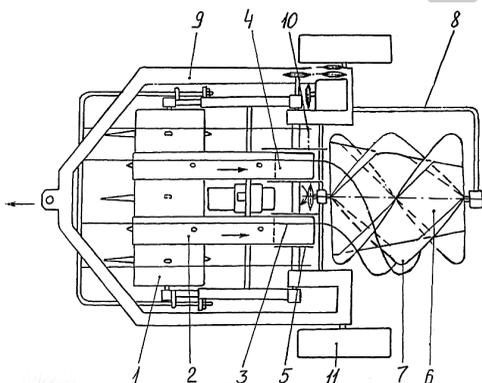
Шнековый оборачиватель (вид сбоку)
